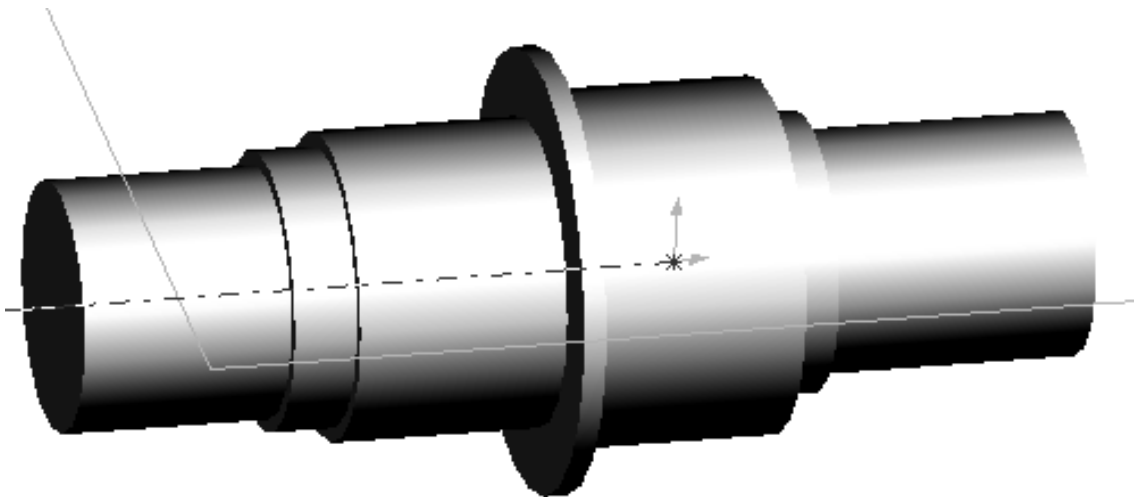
Пример выполнения второго (промежуточного) вала редуктора
